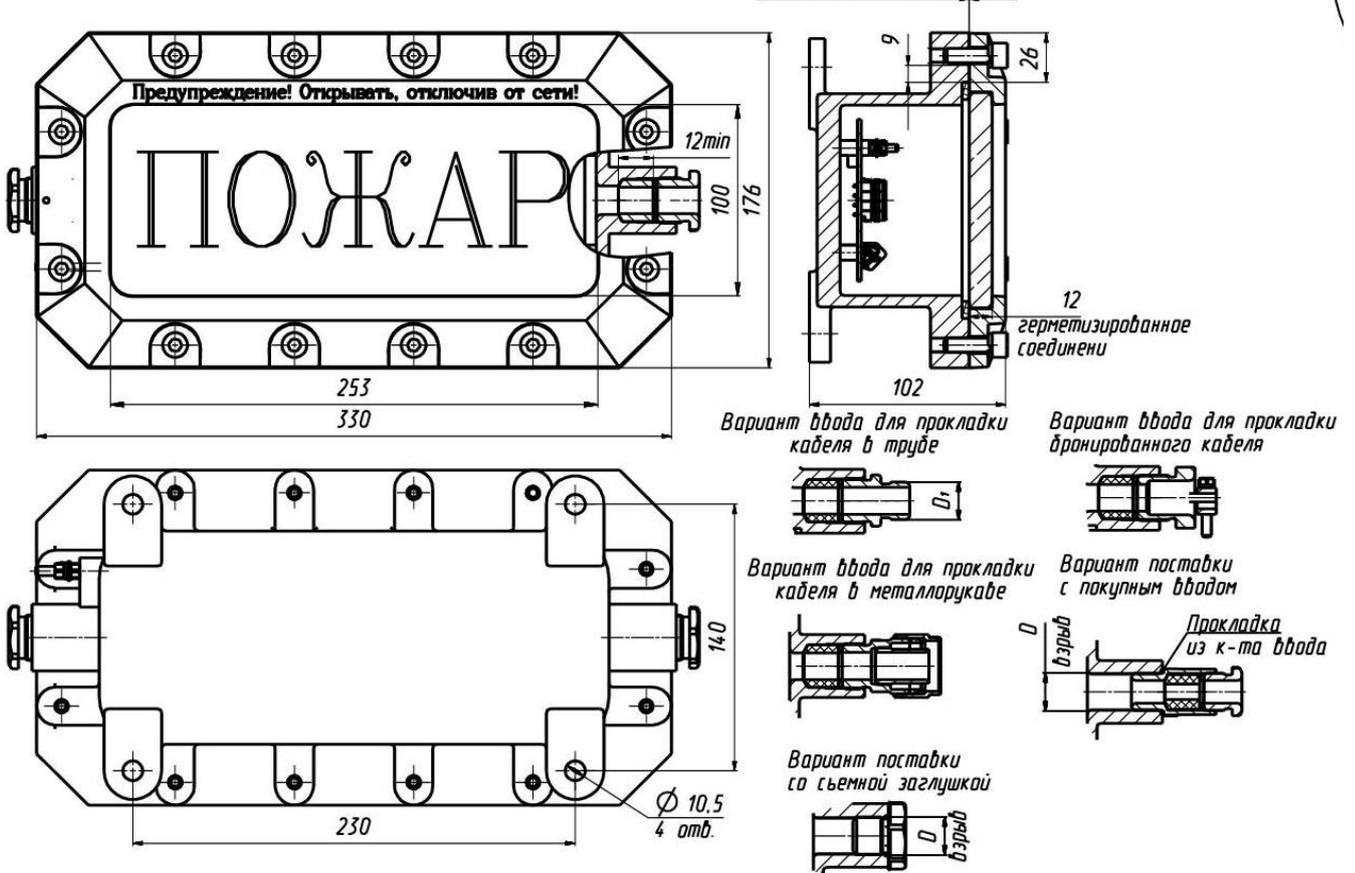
Общий вид с элементами обеспечения взрывозащиты, габаритные, присоединительные размеры табло световых моделей ExTC-1.
